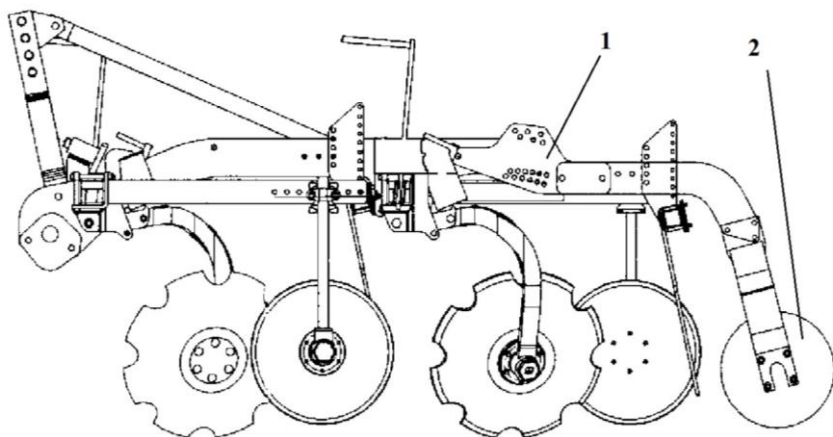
Схема догрузки прикатывающего катка дисковой бороны Рубин 9U фирмы Lemken
